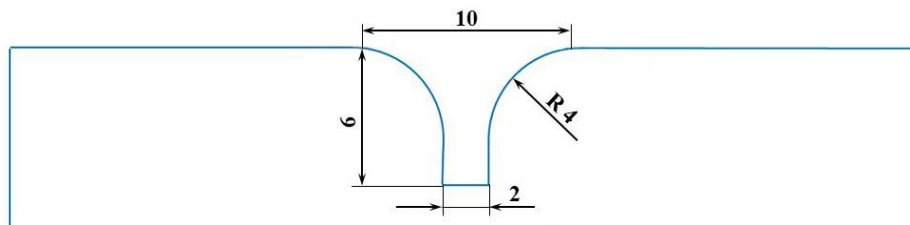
Ескіз форми формуючої канавки в сталевій підкладці, призначеній для плазмо-дугового зварювання алюмінієвих сплавів товщиною 9 – 12 мм.
